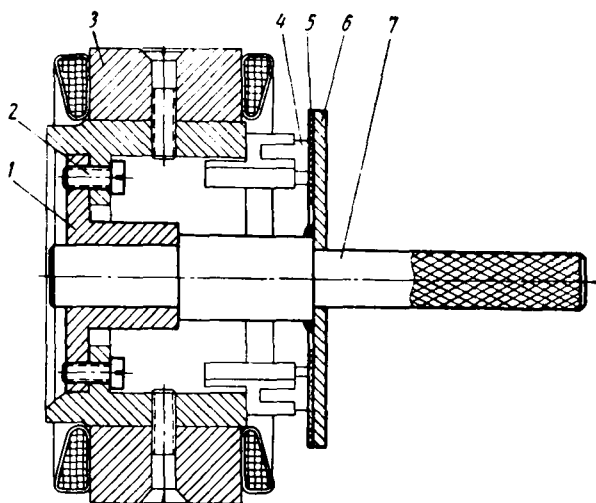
Приспособление для притирки щеток династартера мотороллера Т-200М:
